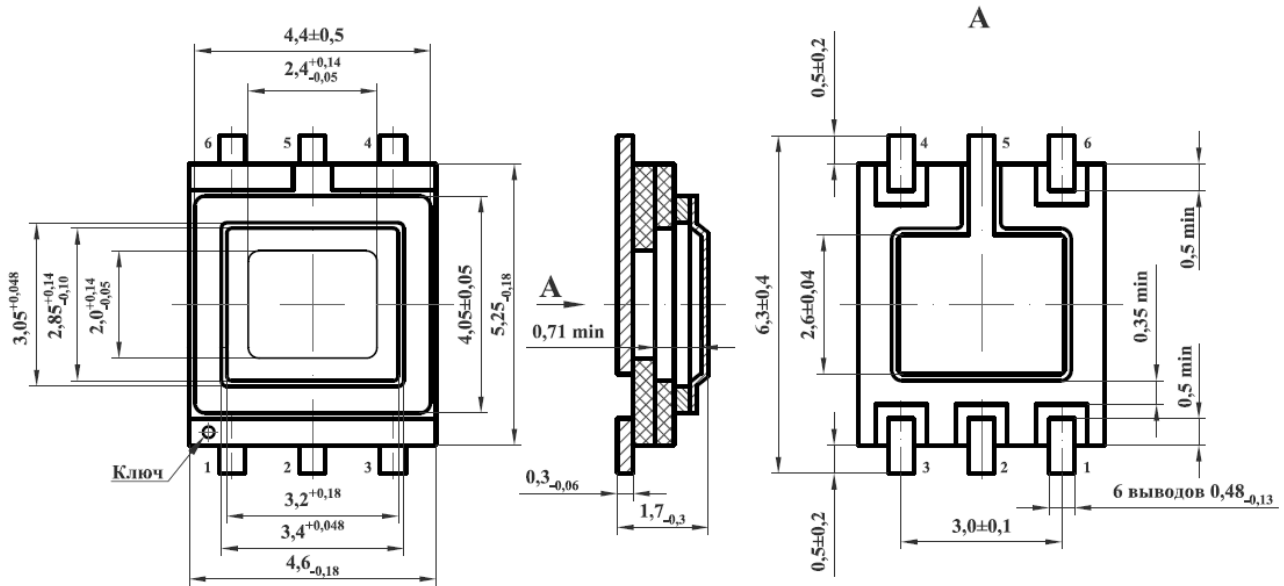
Габаритный чертеж корпуса 5221.6-1 (размеры в мм)
